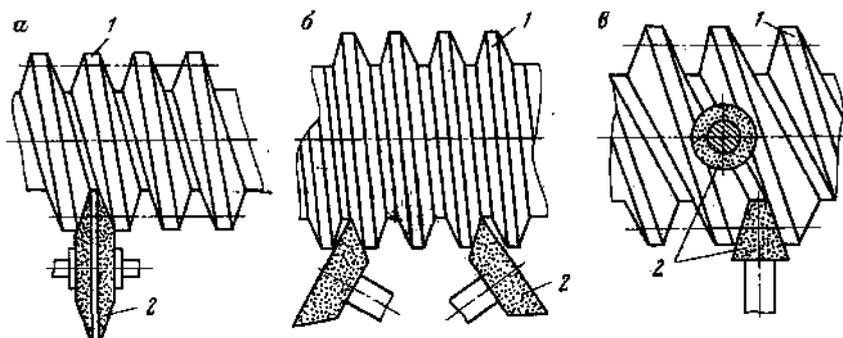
Схема шлифования червяков (1) шлифовальными кругами (2): а - с прямолинейным профилем; б - чашечными; в - пальцевыми
